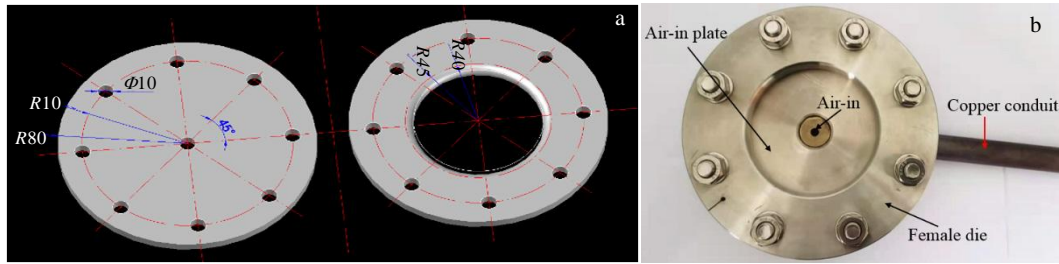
组合式模具 CAD 设计图（进气板和凹模）及工装图
